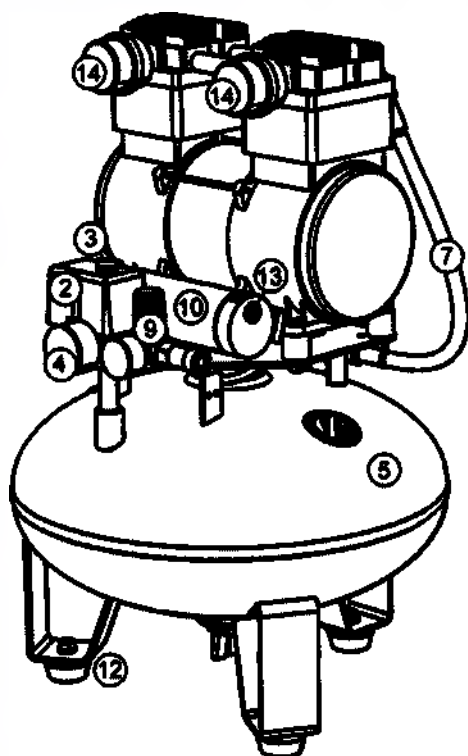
Общий вид компрессора KM-24.OLD15,
